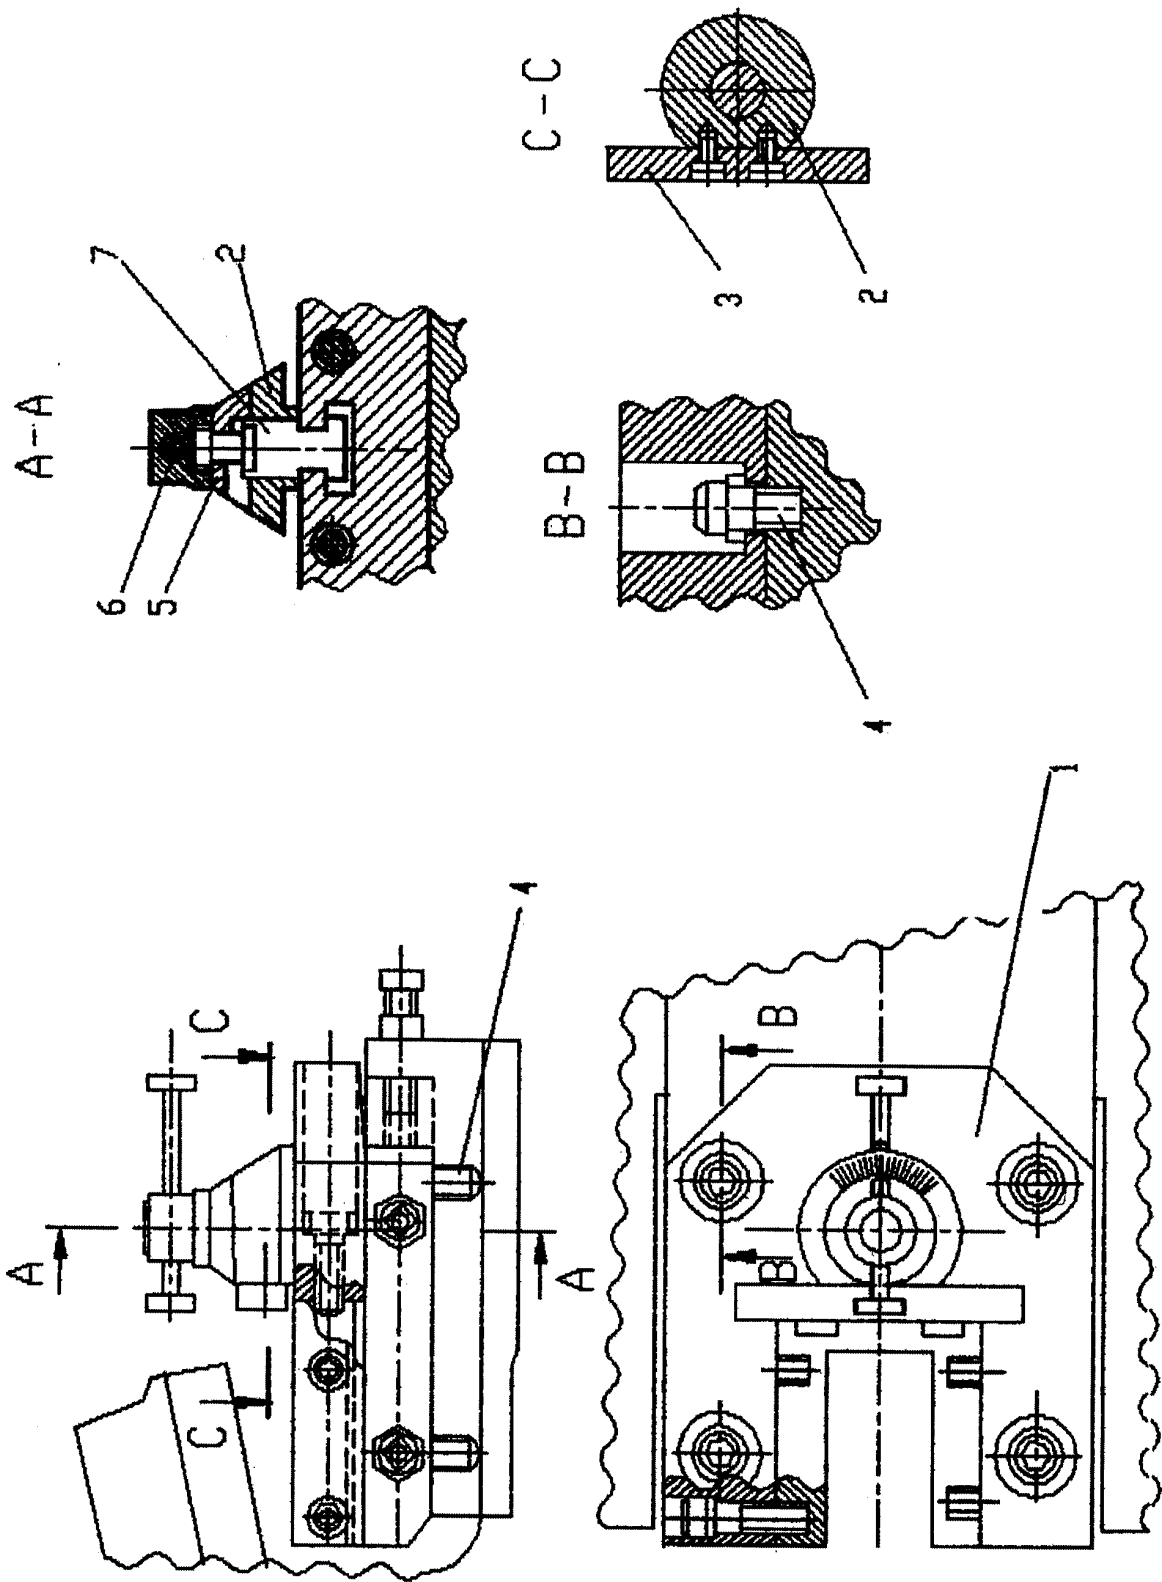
Приспособление для пробивки пазов прямоугольной (треугольной) формы.
